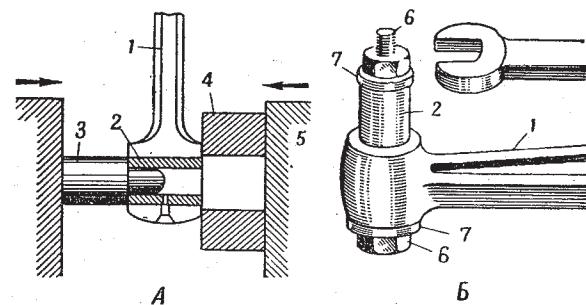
Выпрессовка и запрессовка втулки малой головки шатуна:
